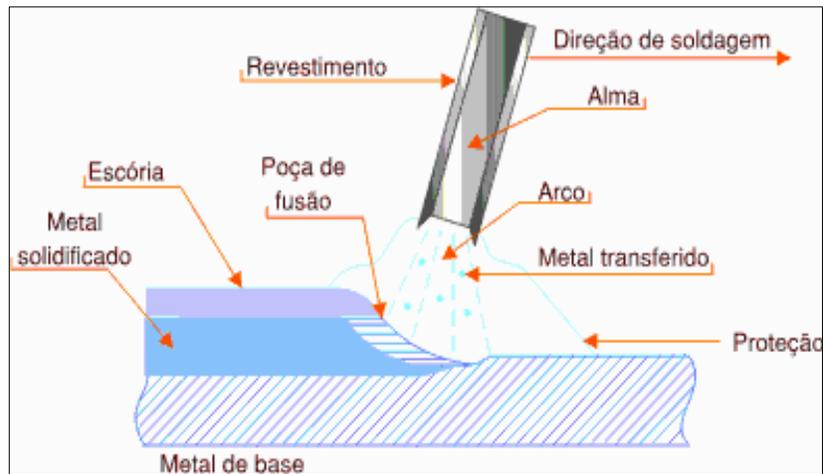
Esquema básico do processo de solda por eletrodo revestido (SMAW) <sup>[69]</sup>.
